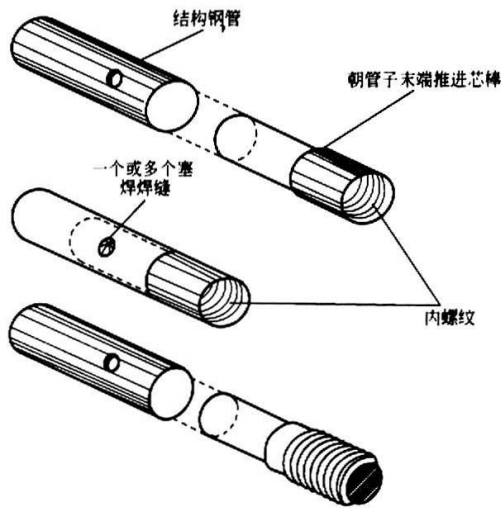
用芯棒和塞焊加工管子螺纹的方法
